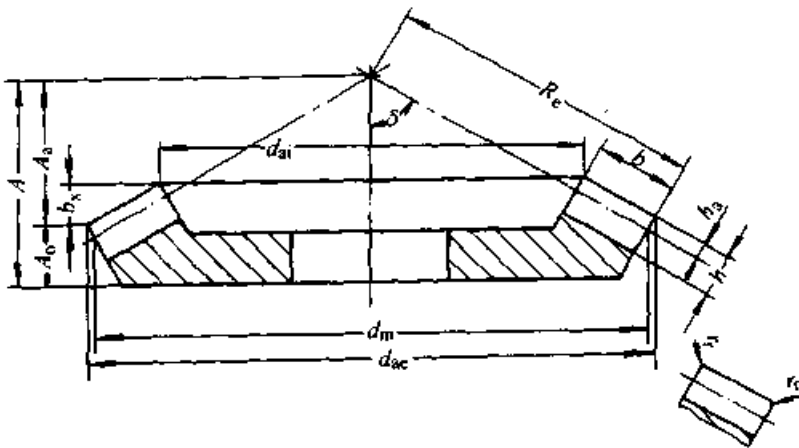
不修正分度锥角、齿顶无倒坡的摆线齿锥齿轮
